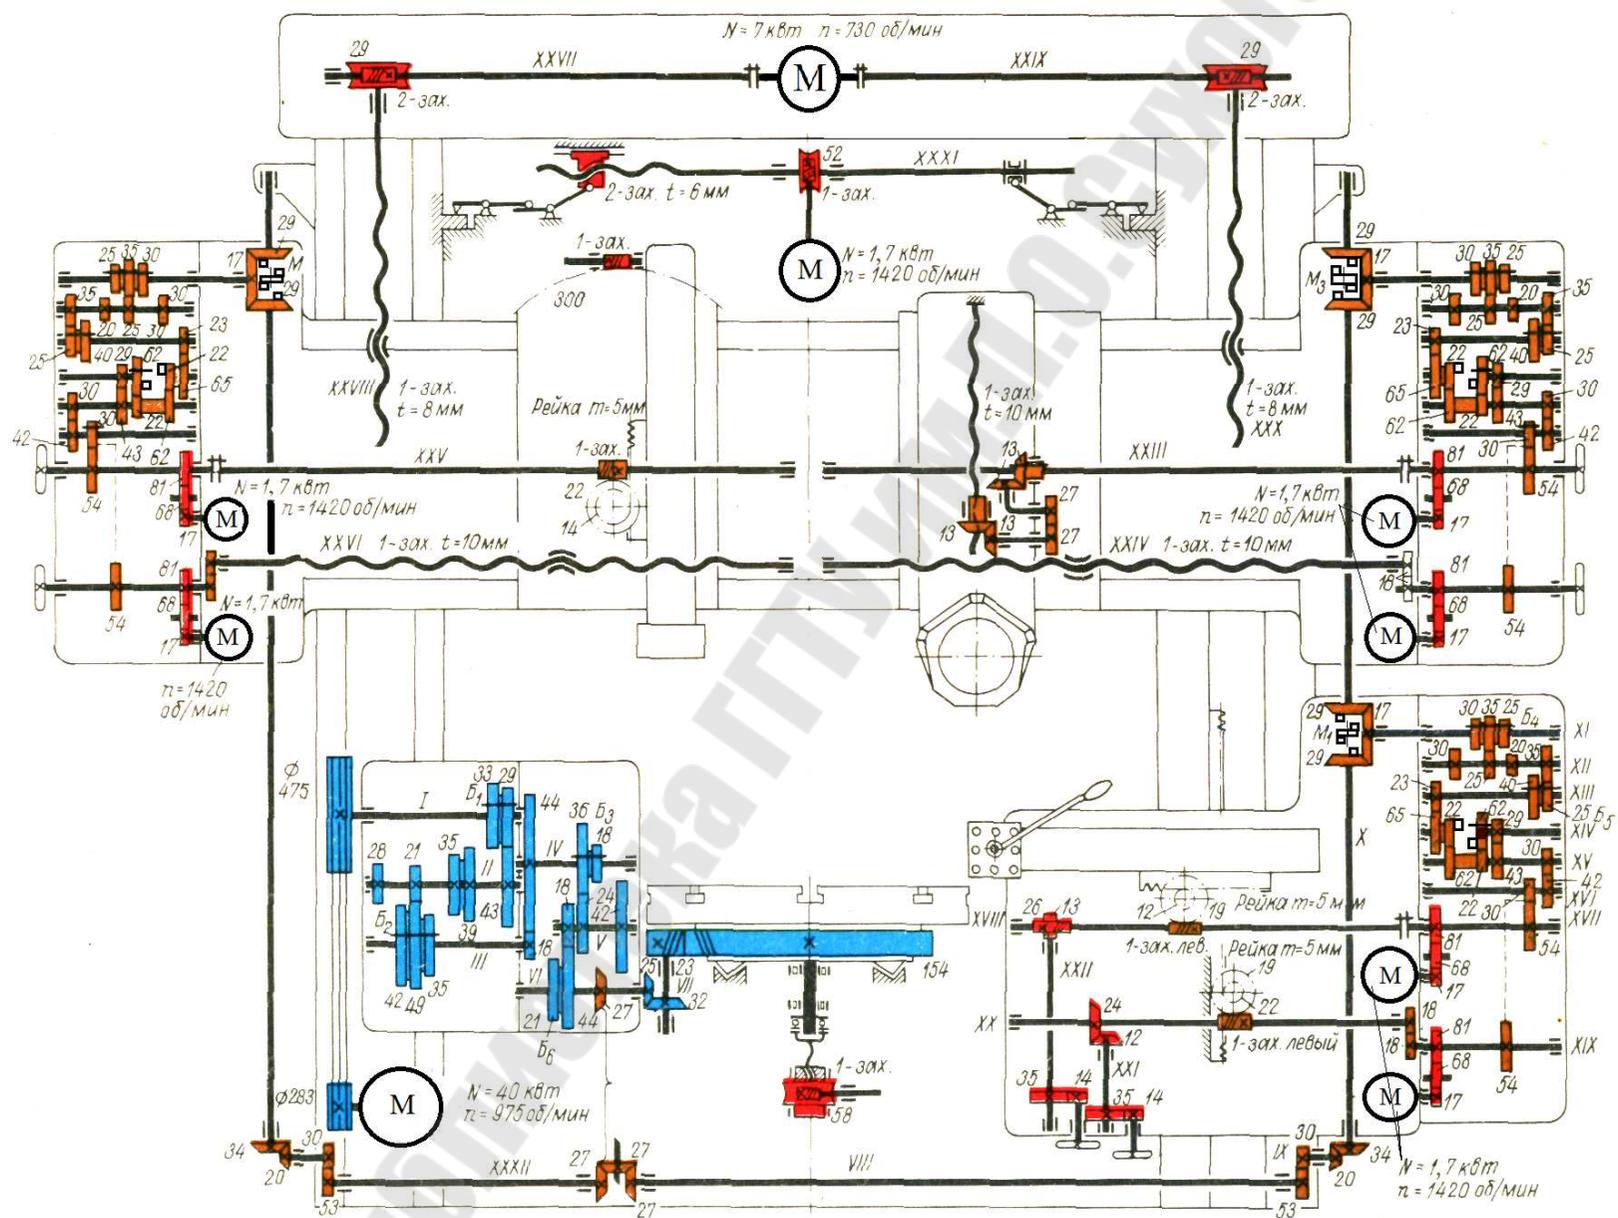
Кинематическая схема токарно-карусельного двухстоечного станка
